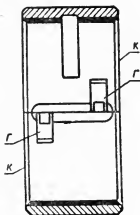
Места маркировки безбуртовых вкладышей коренных подшипников двигателя Д-54:
